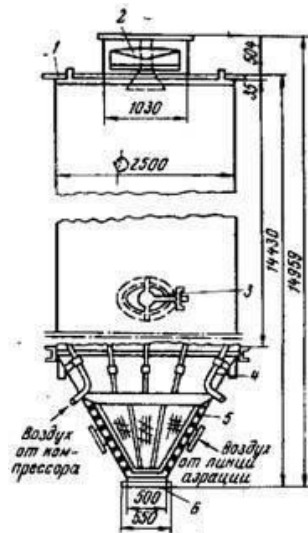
Схема циліндрового бункера ХЕ-160: 1 – загрузочний патрубок 2 – фільтр; 3 – люк; 4 – труби для подачі стислого повітря; 5 – пористе днище; 6 – випускний патрубок
